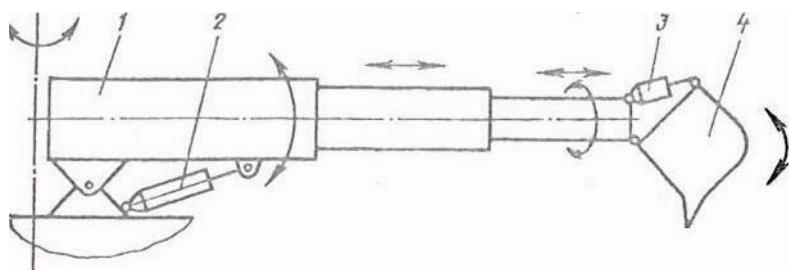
Схема телескопічного робочого обладнання екскаватора:
